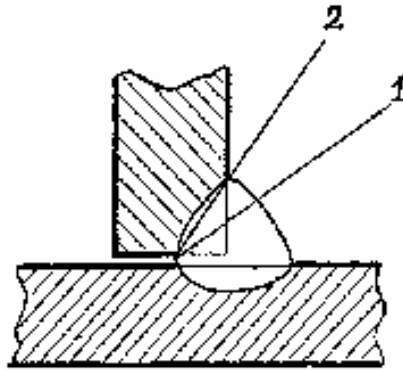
Схема розрахункових перерізів зварного з'єднання з кутовим швом:
